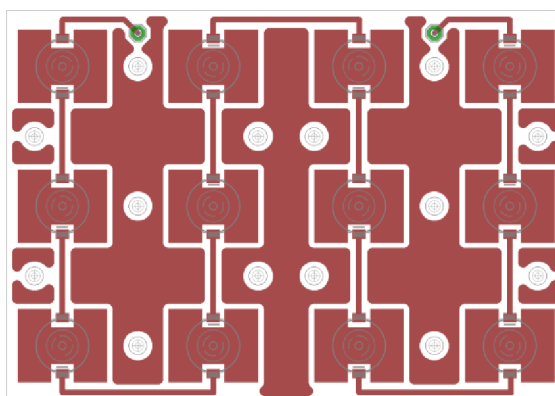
Obrazec spojů navrhnuté napájecí DPS s obrysy součástek
